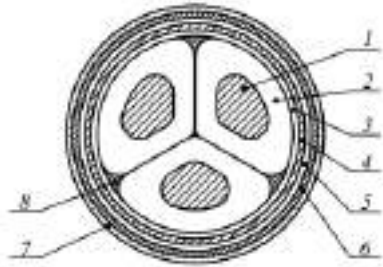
Схема побудови ізоляції кабелю з напругою до 10 кВ.
